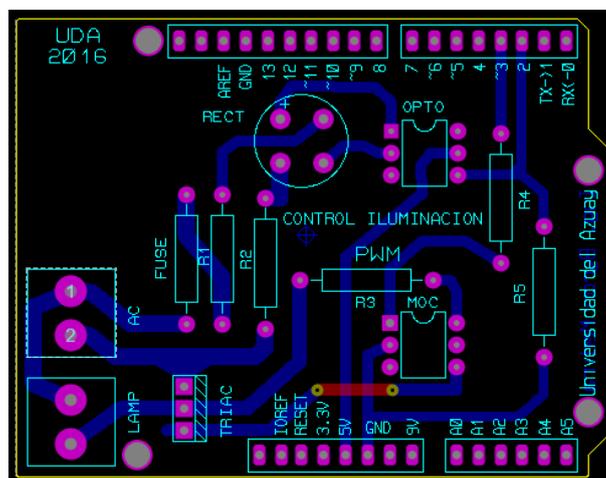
Esquema de la placa con pistas y etiquetas
